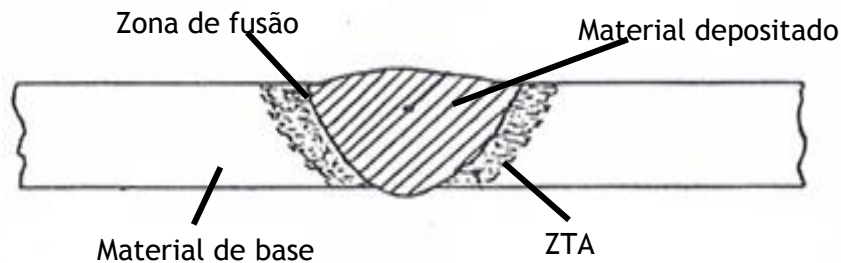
Esquema representativo de um cordão de soldadura habitual [3].
